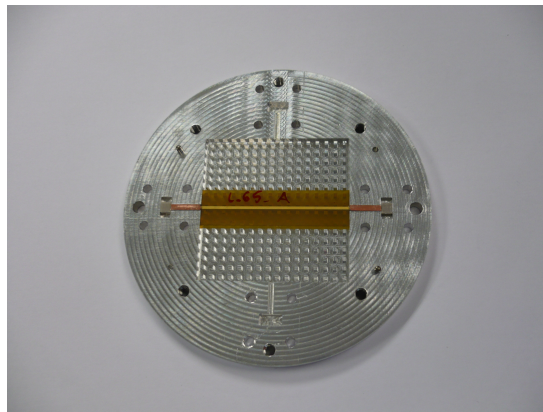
Test-Fixture. Parte inferior con el circuito Suspended-Strip montado.
